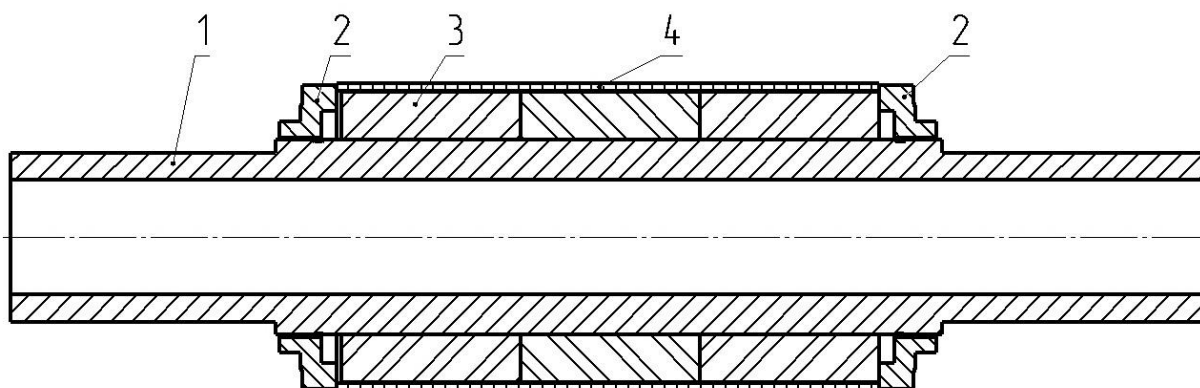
Эскиз магнитной системы ротора с немагнитной шихтованной обоймой: 1- вал (ядро), 2- гайка, 3 – постоянный магнит, 4 – немагнитный кольцевая пластина.
